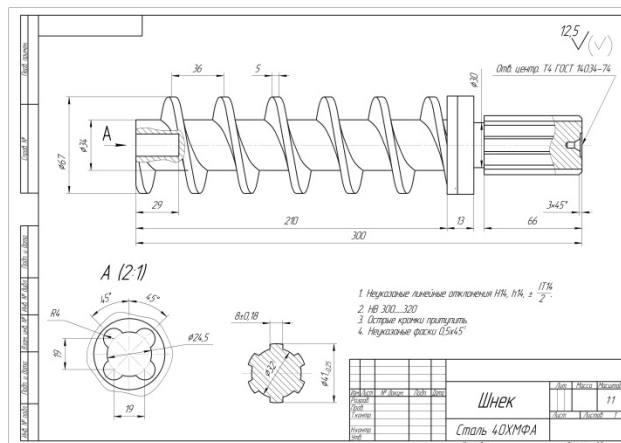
Креслення модернізованого шліцьового шнека, виготовленого методом механічної обробки
